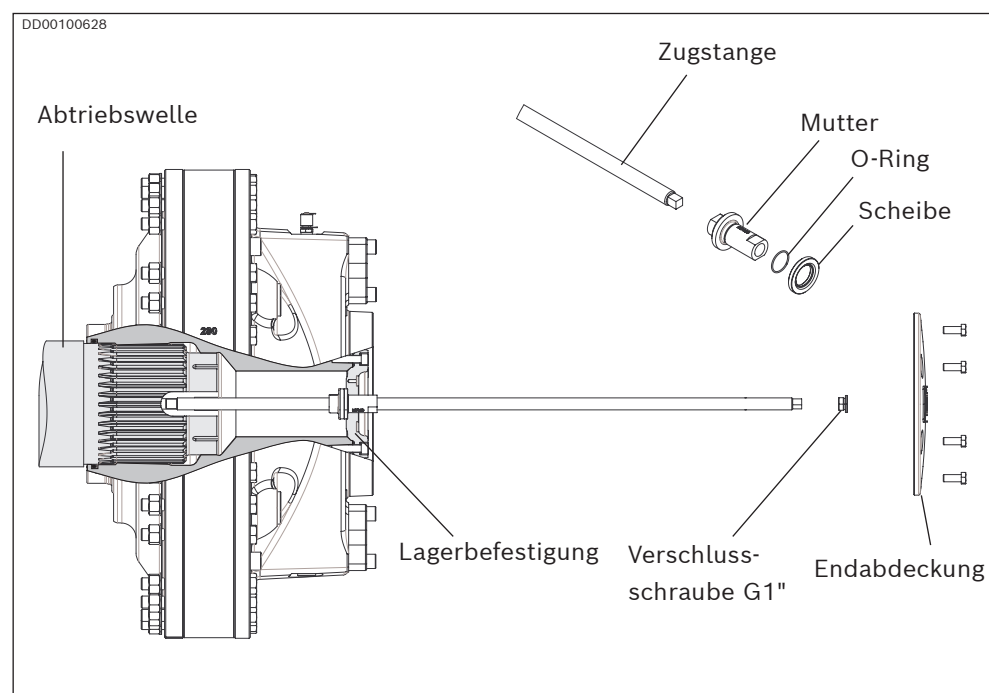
Montagewerkzeug zur Demontage des CB Motors mit Vielkeilnut
